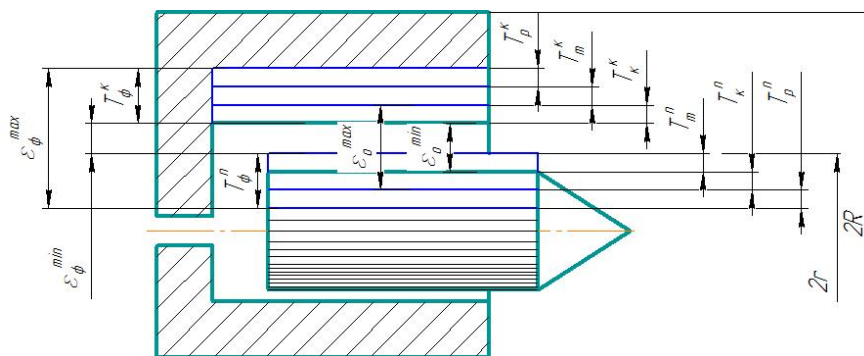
Схема расположения допусков поршневой пары аксиально-поршневой гидромашины
